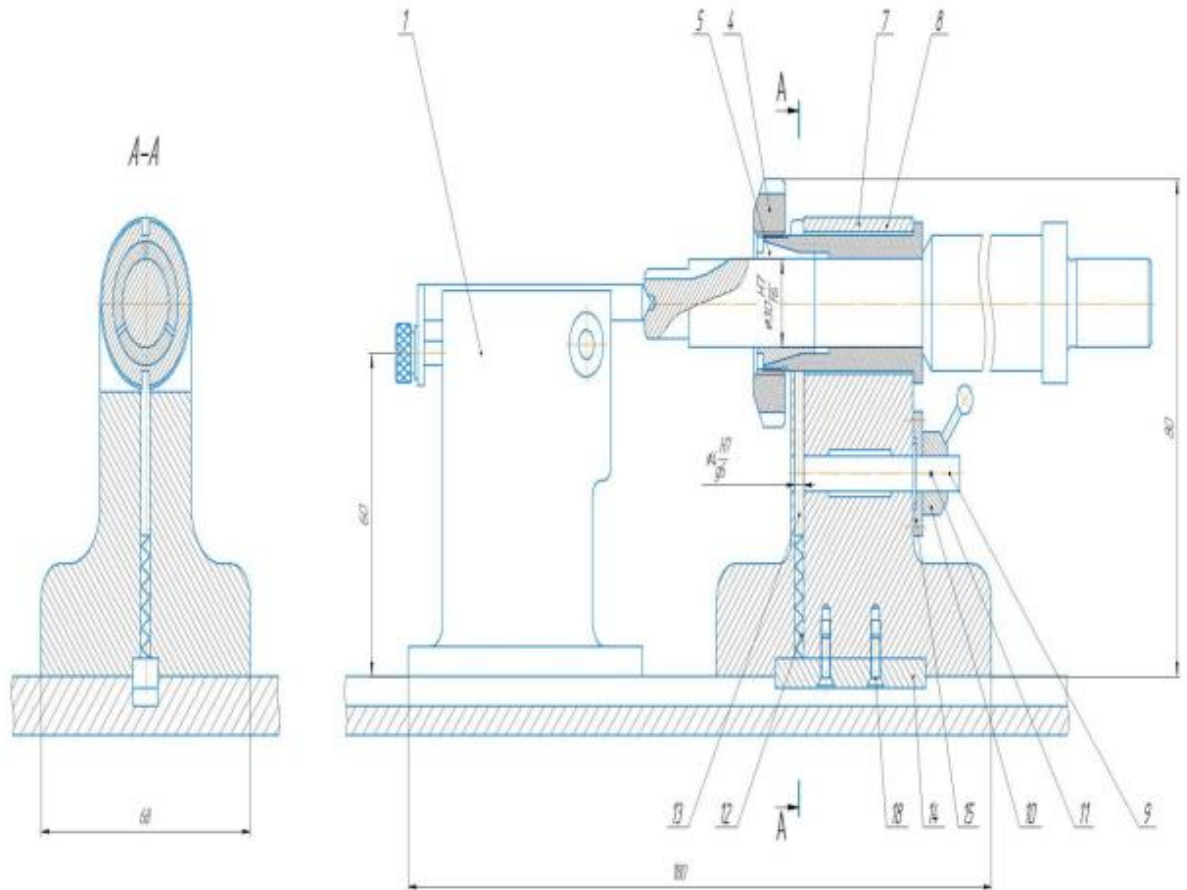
Компонировка приспособления приведен на листе формата А3
